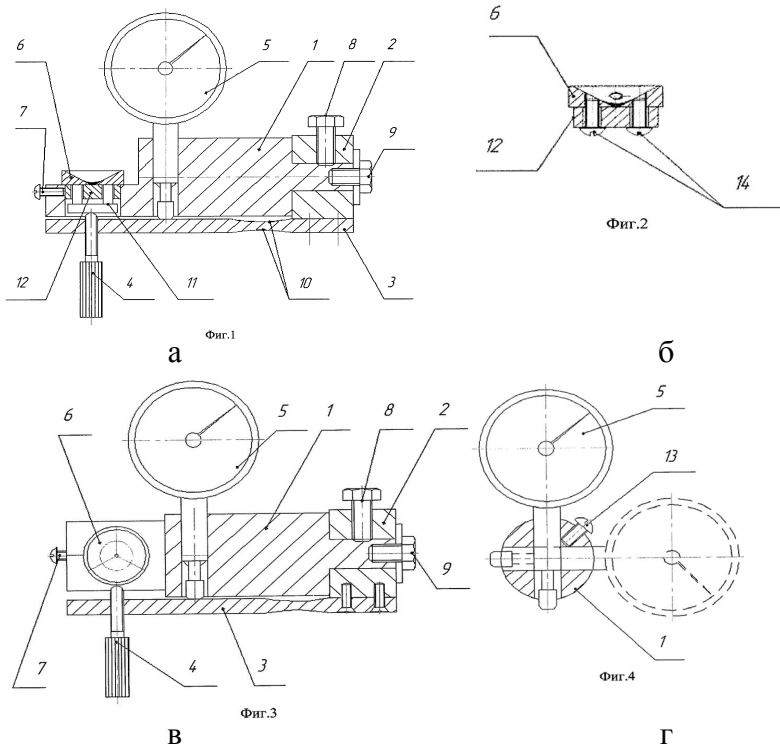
Устройство с фиксатором и калиброванным отверстием (а – общая схема, б – отрывной элемент, в – общая схема – рабочее состояние, г – измерительное устройство). 1 - поворотный элемент, 2 - основание, 3 - пружина, 4 - нагружающий винт, 5 - индикатор, 6 - отрывной элемент, 7 - фиксирующий винт, 8 - позиционирующий болт, 9 - стягивающий болт, 10 - тензорезисторы, 11 - толкатель, 12 - подложка, 13, 14 - фиксирующие винты.
